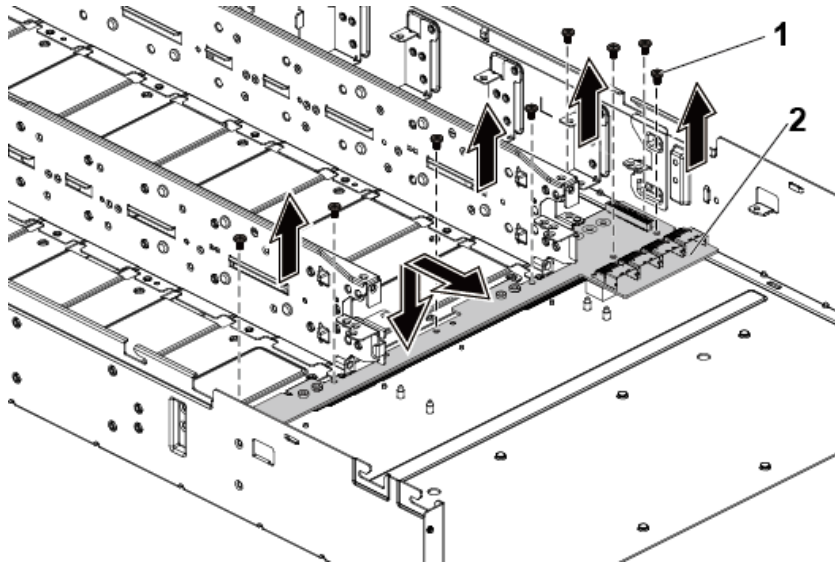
Entfernen des Mittelplatten-Halters
